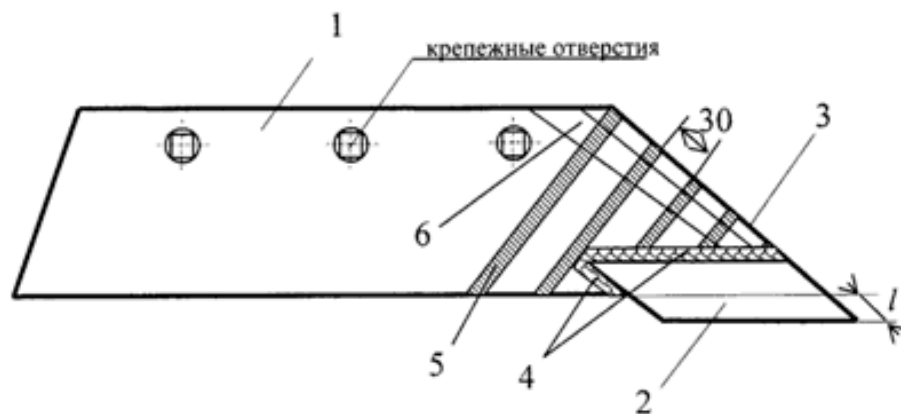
Схема восстановления лемеха (1 - рабочая поверхность; 2 - приваренная стальная пластина; 3 - полевой обрез; 4 - сварные швы; 5 - армирующие валики; 6 - область лучевидного износа).
